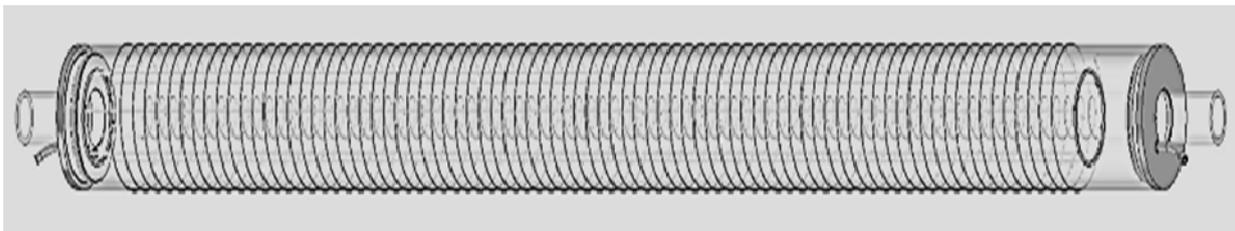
Внешний вид реактора с цилиндрической геометрией
